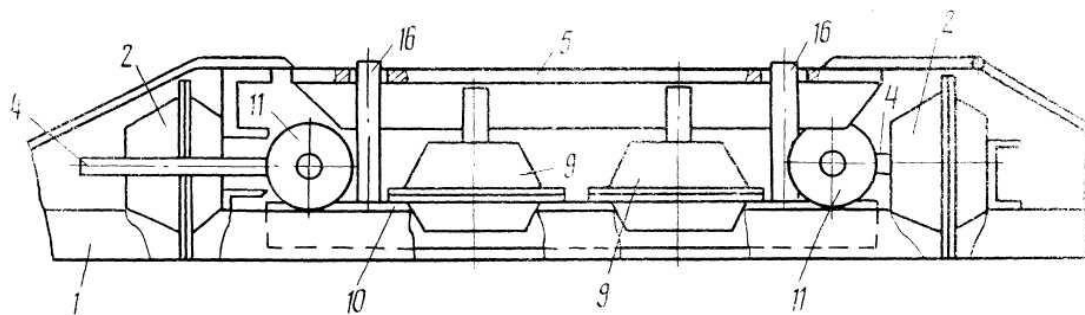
Схема конкретного исполнения стенда, вид сбоку
